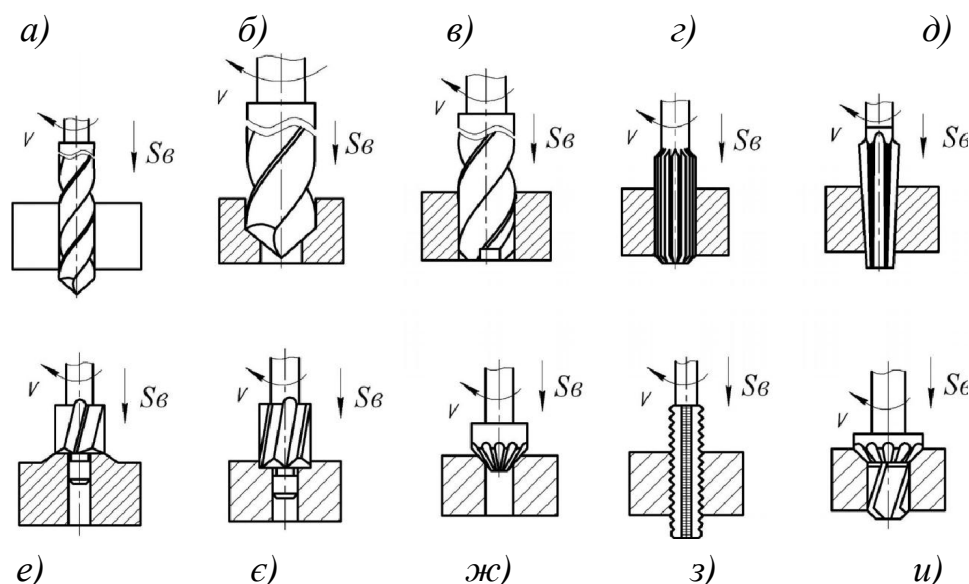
Схеми обробки заготовок на свердлильних верстатах
